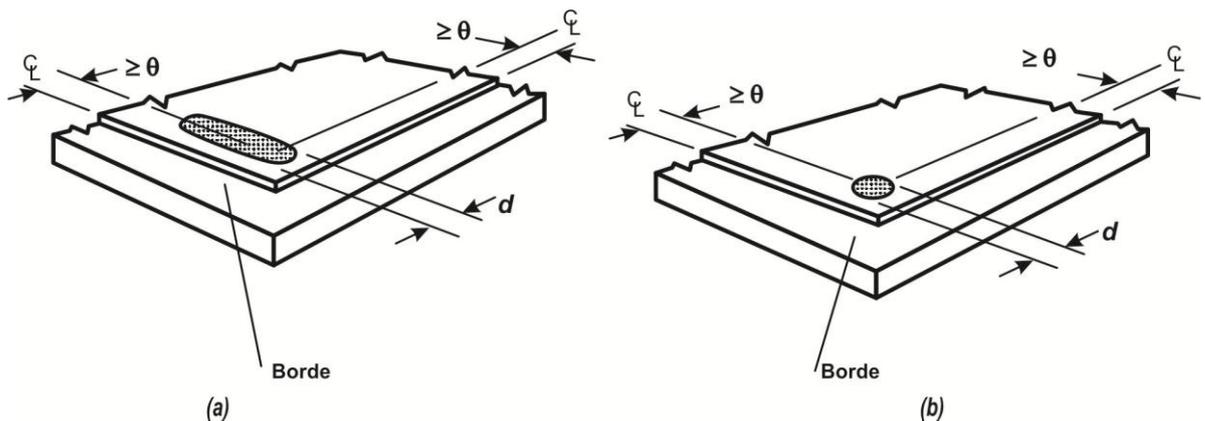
Distancia a los bordes para soldadura de costura (a) y para soldadura de botón (b).
